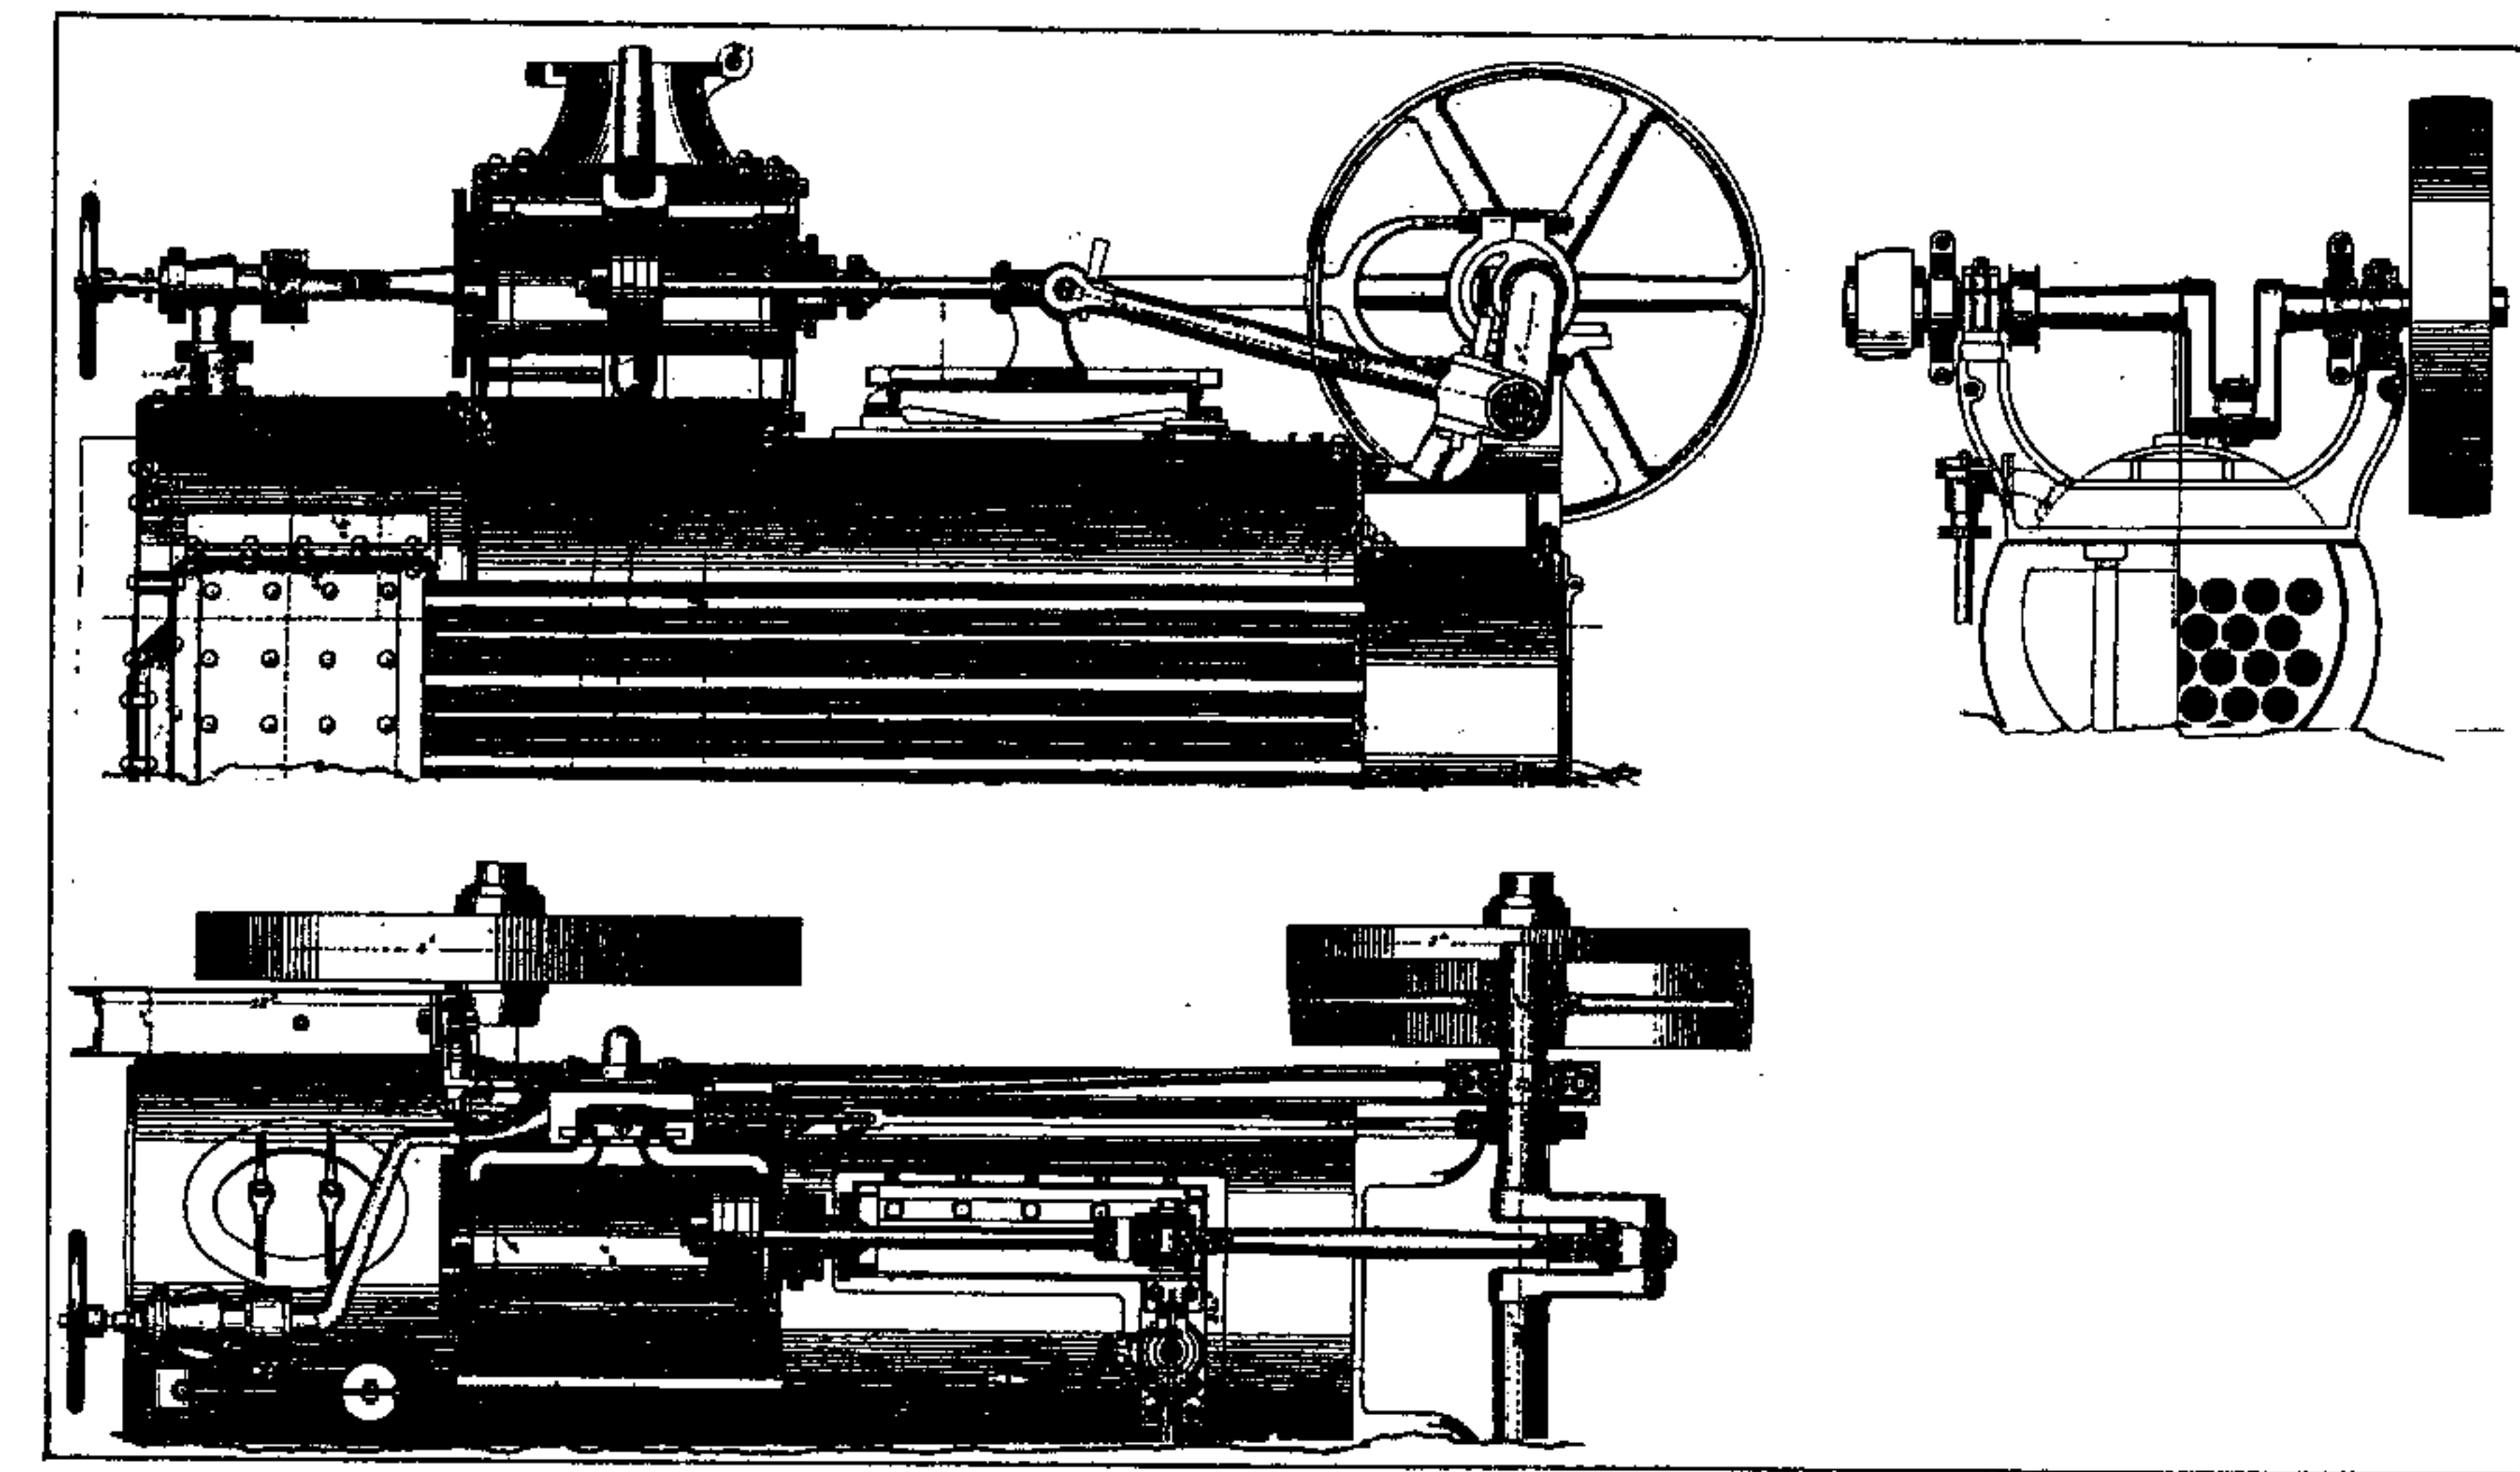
/5: Lokomobilmaschine von A. Borsig (1864)
